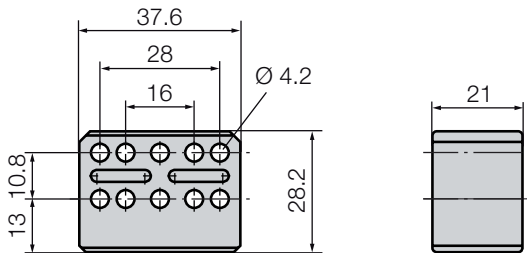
Dimensions de montage du capteur de position BTL6-A-3800-2
